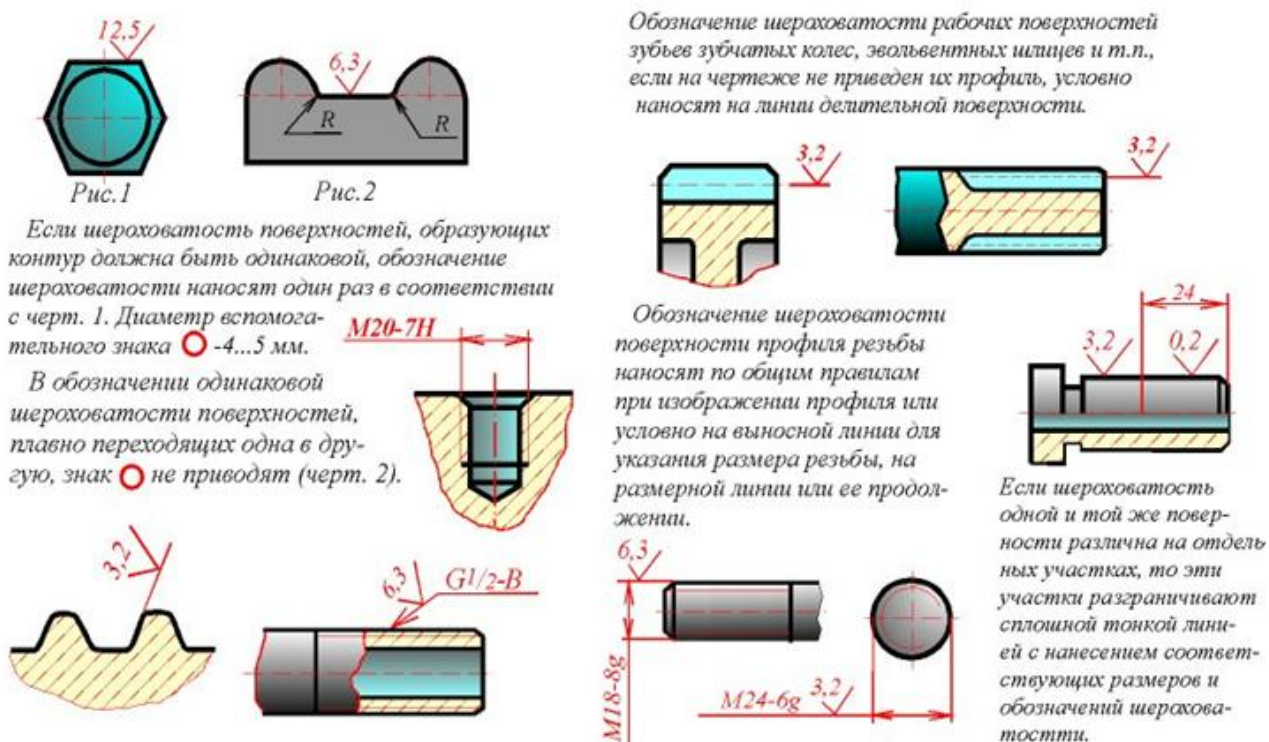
Обозначение шероховатости поверхностей, образующих замкнутый контур
